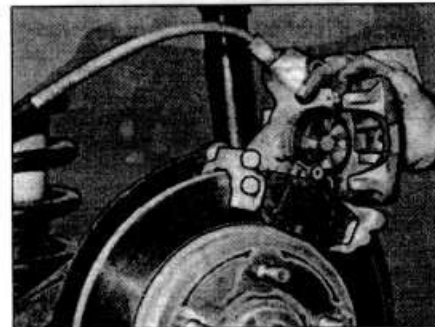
Поворачивание суппорта при снятии тормозных колодок тормозного механизма заднего колеса
